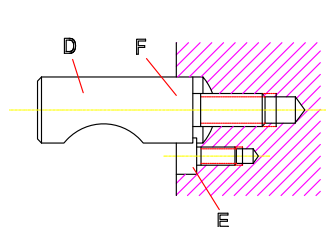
Dispositivo de fijación con leva de bloqueo
